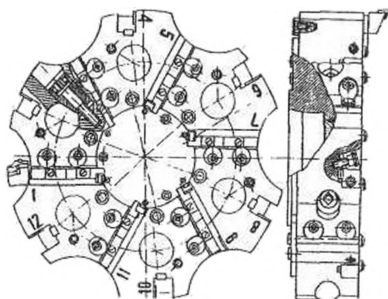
Уніфікована револьверна головка для токарних верстатів з ЧПУ для закріплення інструментів з осьовим і радіальним розташуванням
